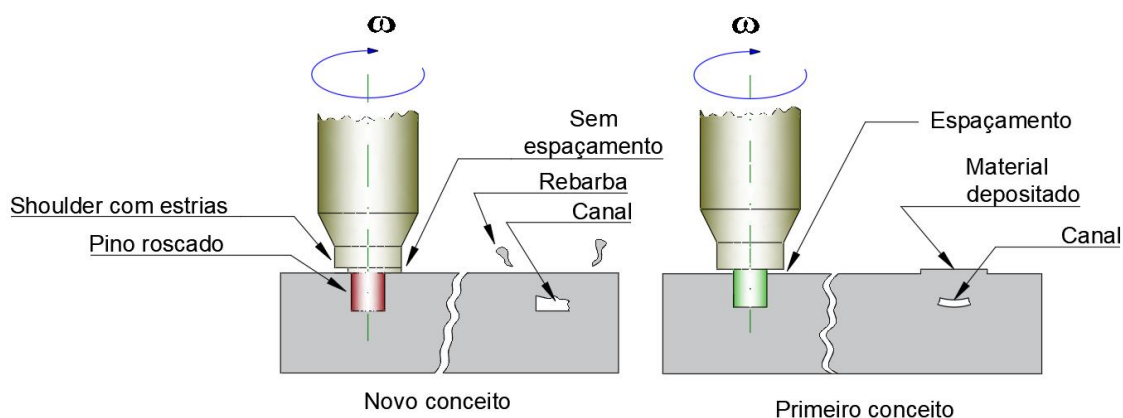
Representação esquemática do *FSC without shoulder clearance* (esquerda) e do *FSC with shoulder clearance* (direita), adaptado de [18]
